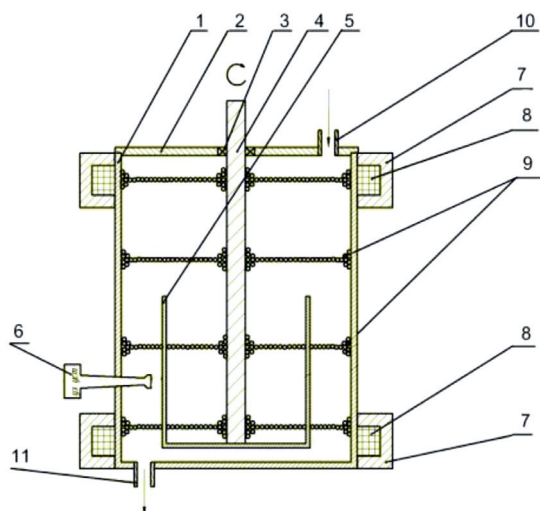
Конструктивная схема смесителя ЭМС-2 (Патент России на полезную модель № 86493): 1 – цилиндрическая камера; 2 – крышка; 3 – подшипник; 4 – ротор; 5 – лопасти; 6 – источник УЗ; 7 – ферромагнитное кольцо; 8 – ОУ; 9 – ферромагнитные цилиндры; 10, 11 – патрубки для входа и выхода смеси
